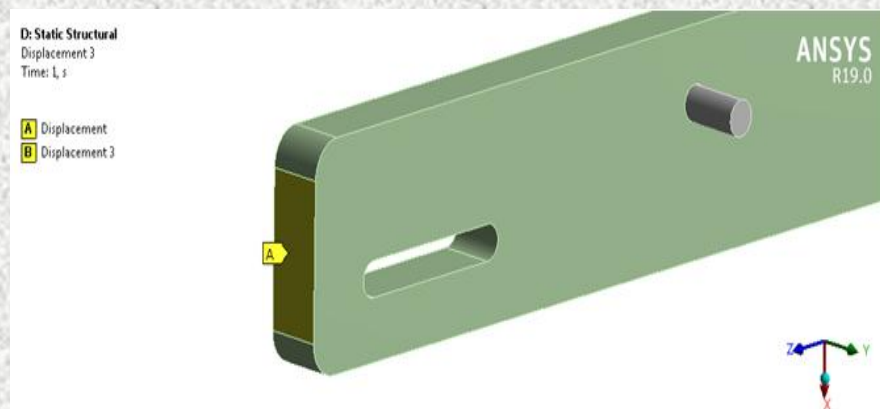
Закрепления боковых поверхностей по оси Y и Z
